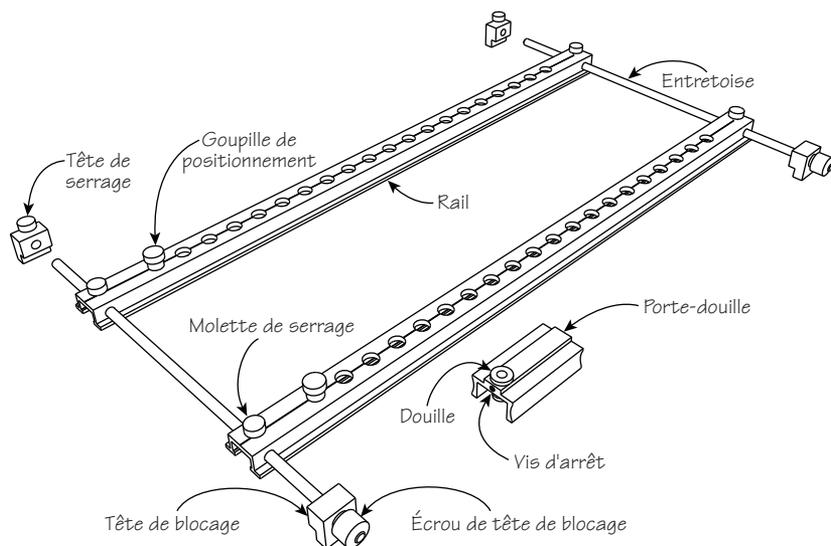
Assemblage du gabarit de perçage pour tablettes
